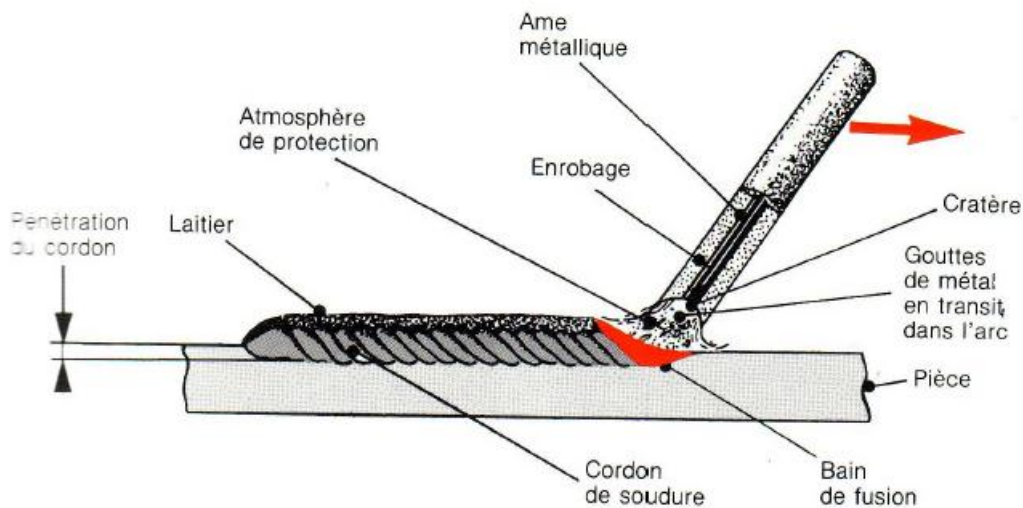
Schémas explicatif du procédé du soudage à l'arc.
